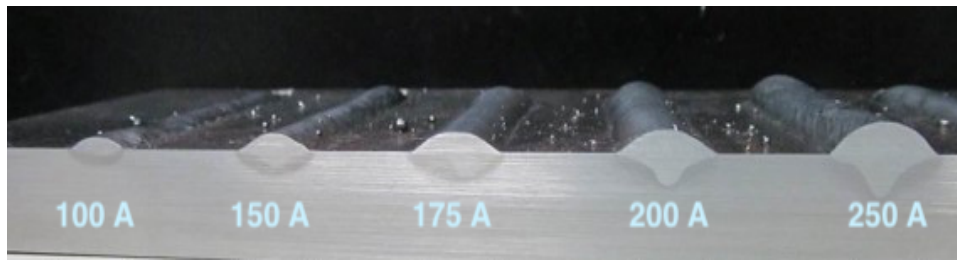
Profondeur de pénétration pour quelques courants de soudage
